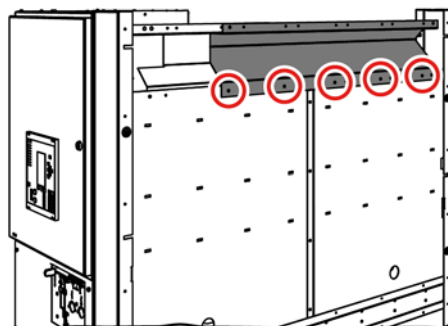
Точки крепления длинной металлической пластины для защиты от аварийной электрической дуги
